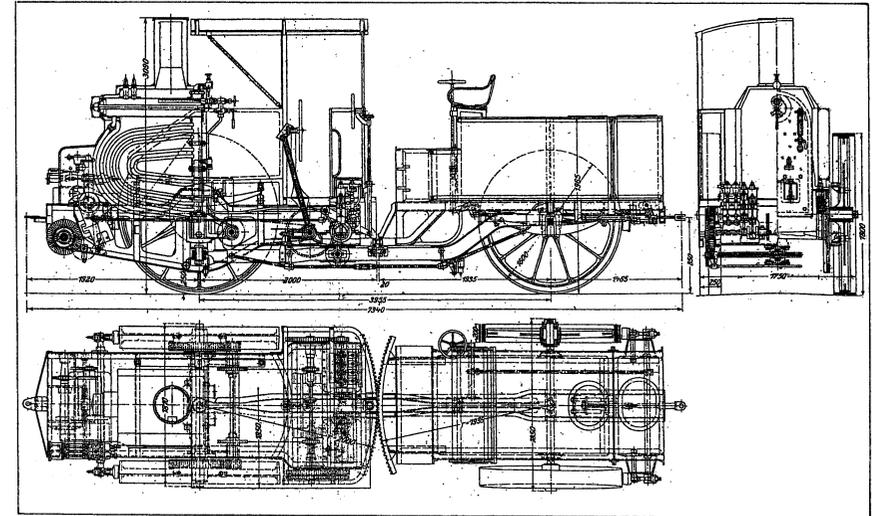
/1: Zeichnung der Zugmaschine eines Freibahnzuges (1906)
